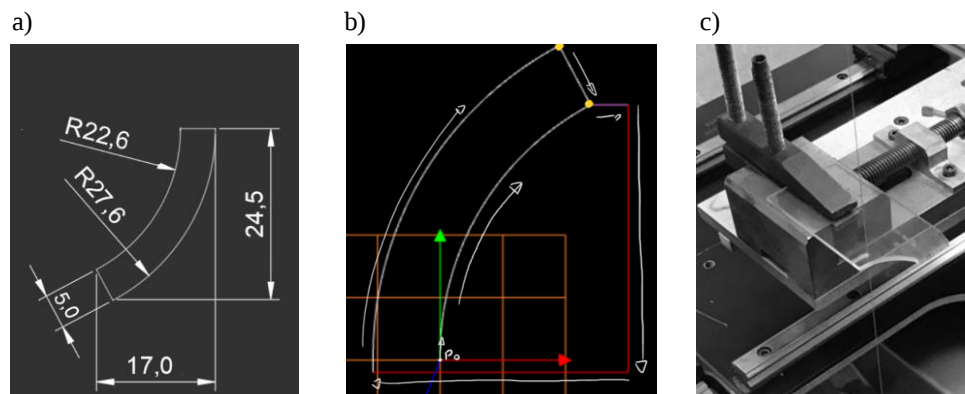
a) geometria e dimensões da peça; b) trajetória de usinagem do arco ; c) processo de corte.
